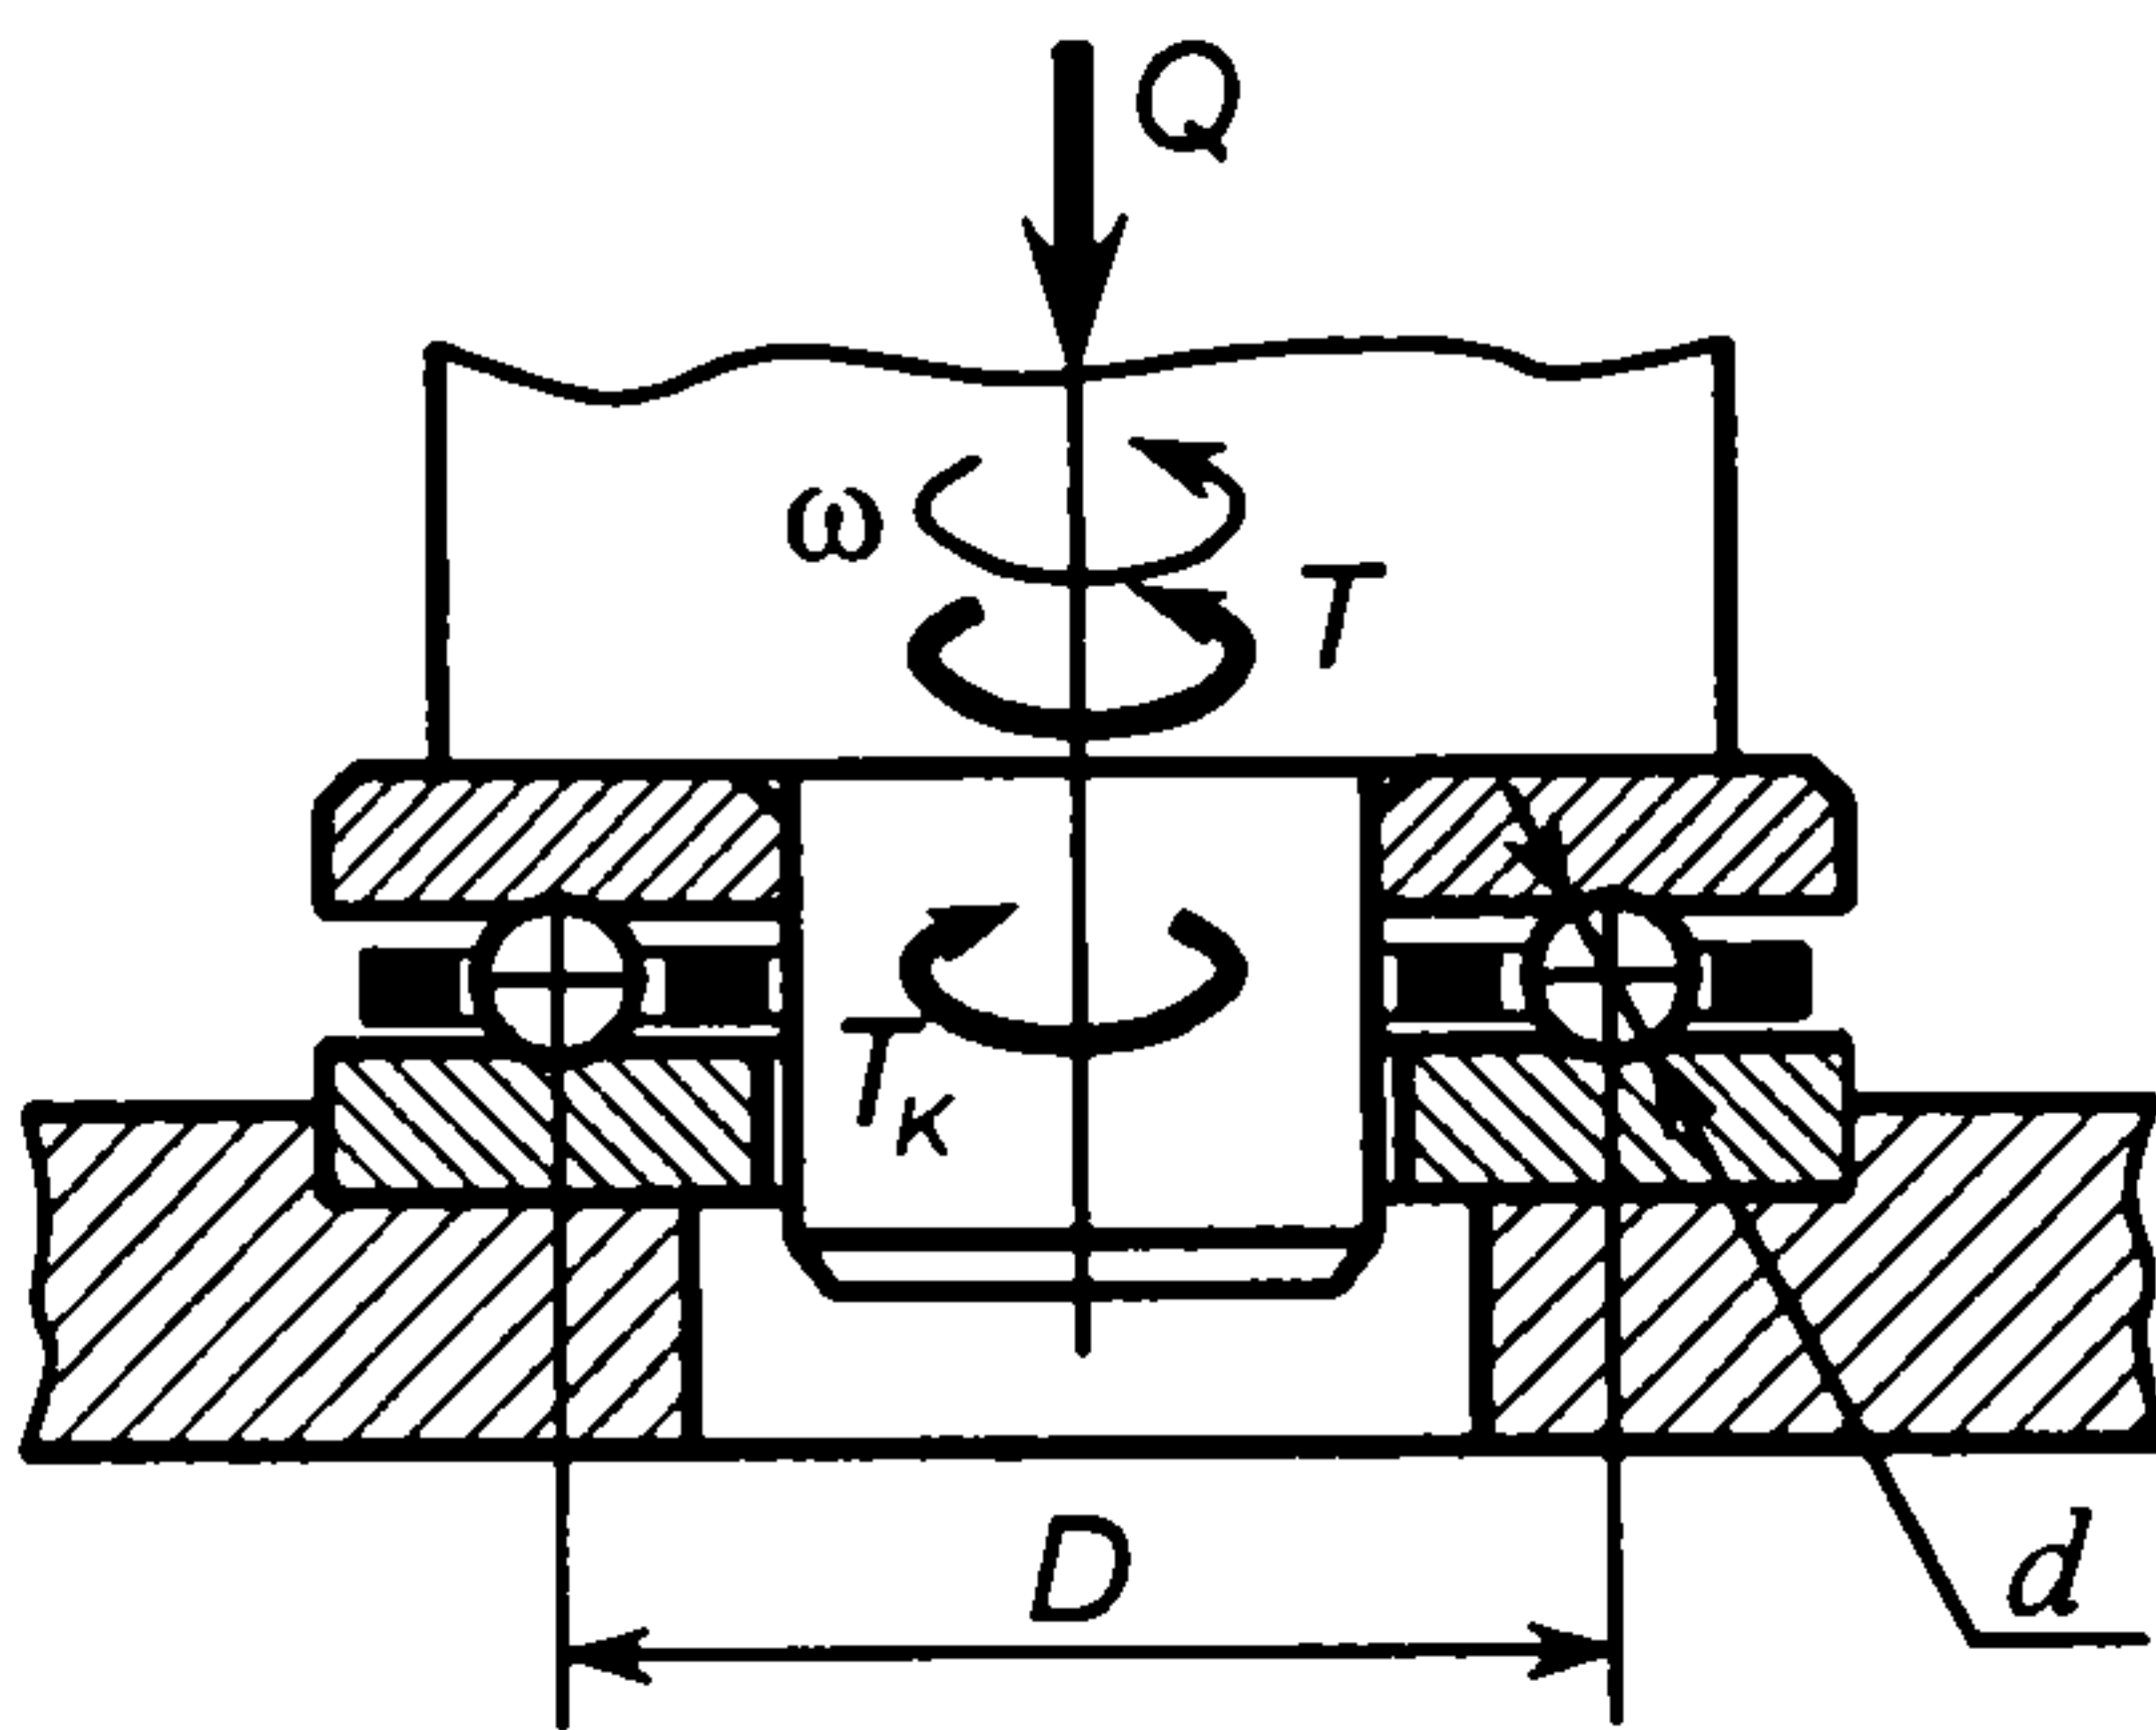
Опора вала на упорному кульковому підшипнику
